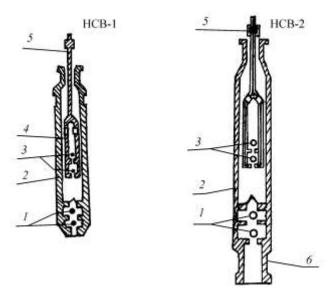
Насосы скважинные вставные: 1 – впускной клапан; 2 – цилиндр; 3 – нагнетательный клапан; 4 – плунжер; 5 – штанга; 6 – замок
